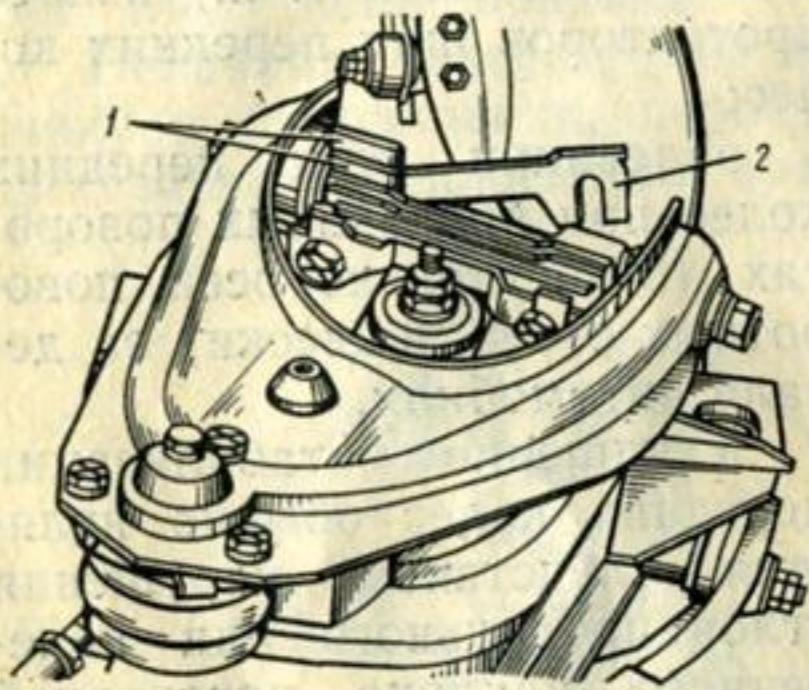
Регулировка углов продольного наклона поворотной стойки подвески и развала переднего колеса:
